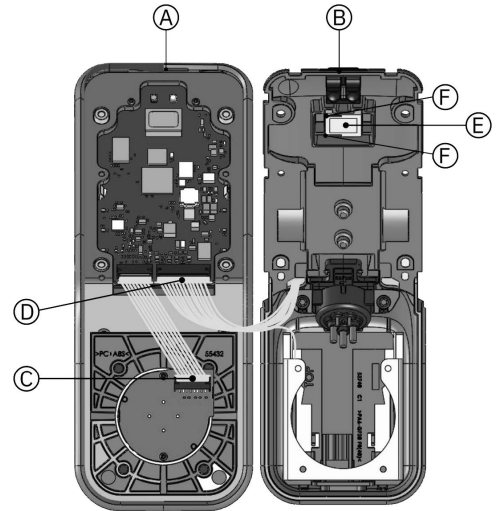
Wiederanschießen der Steckverbinder und Schließen des Gehäuses
